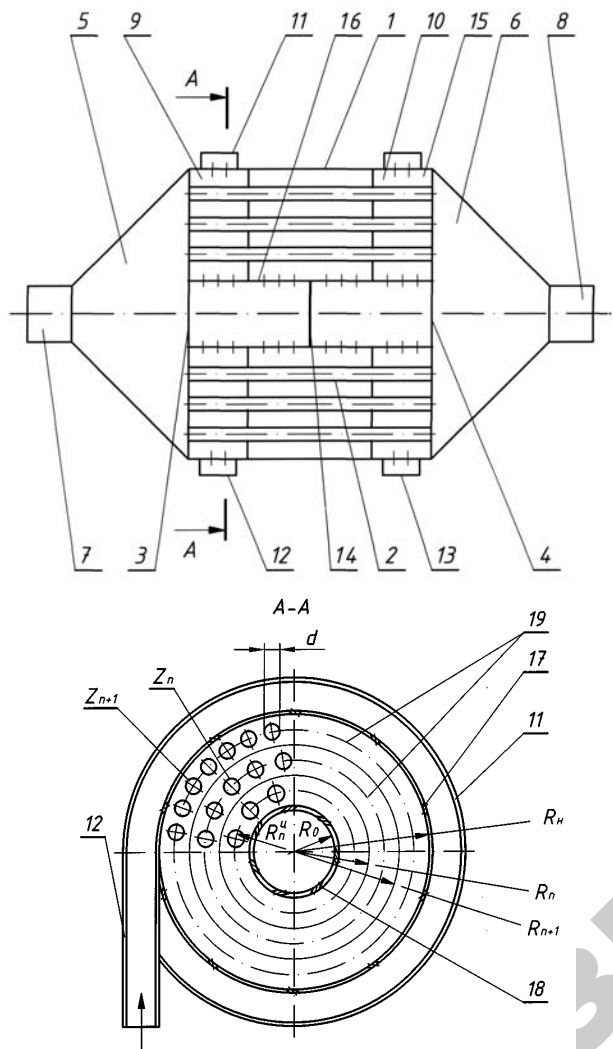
Схема кожухотрубчатого теплообменника: 1 – кожух; 2 – трубы теплообменные; 3, 4 – решетки трубные; 5, 6 – камеры; 7, 8 – патрубки; 9, 10 – камеры; 11 – обечайка кольцевая; 12, 13 – патрубки; 14 – перегородка; 15 – отсек; 16 – коллектор; 17, 18 – отверстия; 19 – кольца условные; d – диаметр трубы; R_n – радиус наружный; R_n – радиус n -го условного кольца; Z_n – число отверстий на n -м условном кольце; R_0 – радиус коллектора; R_n^n – центральный радиус n -го условного кольца
